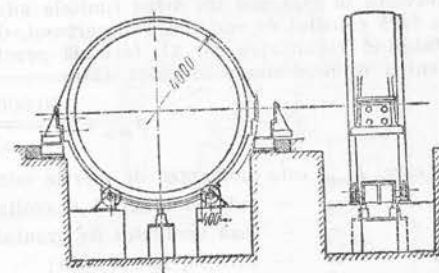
Carcasă cu tălpile înșurubate, montate pe role.
